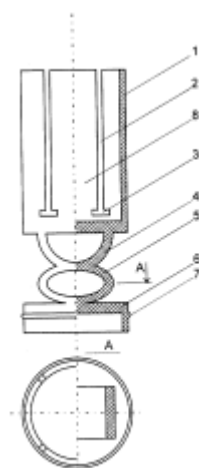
Устройство пыжа – контейнера: 1- дробовой контейнер; 2- продольные прорезы; 3-поперечные прорезы; 4-компенсатор 5-трубчатый амортизатор; 6-поршень - obtюратор; 7-obтjрирующий поясok; 8-лепестки.
